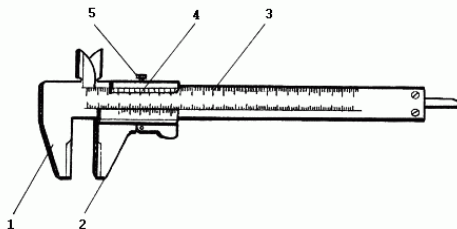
Штангенциркуль: 1 – измерительные губки; 2 – рамка; 3 – штанга; 4 – нониус; 5 – стопорный винт
